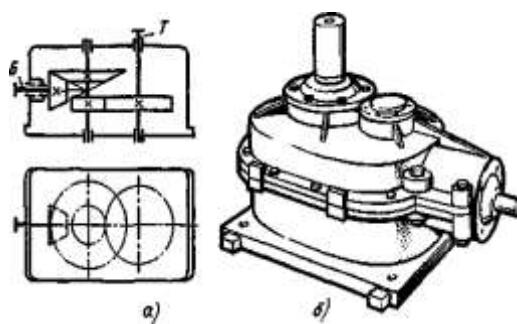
Двухступенчатый коническо-цилиндрический редуктор с вертикальным тихоходным валом: а — кинематическая схема; б — общий вид
